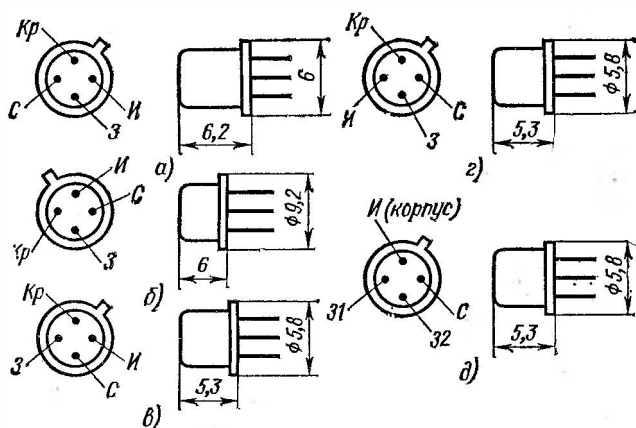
Цоколевка и основные размеры кремниевых полевых транзисторов:
